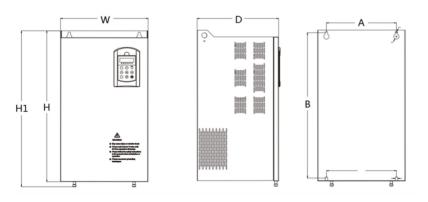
C300系列 11kW~400kW外型尺寸及安装尺寸示意图
